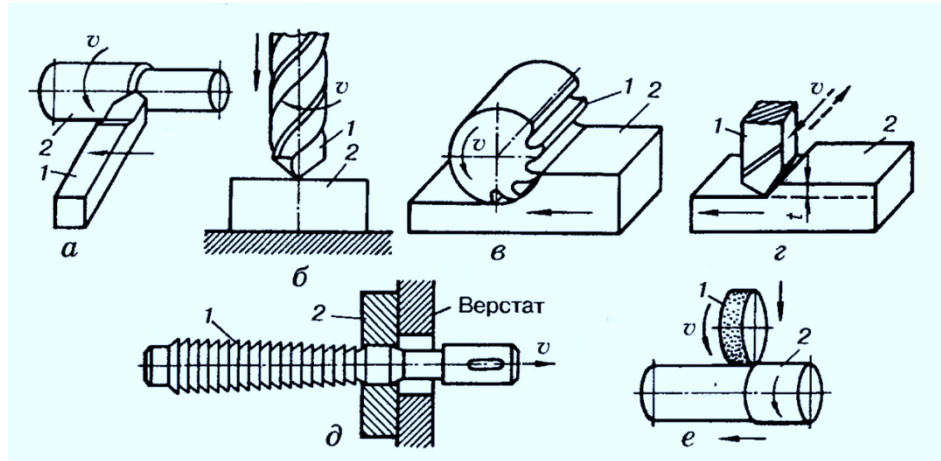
Схеми основних методів обробки різанням: а) - точіння, б) - свердління, в) - фрезерування, г) - стругання, д) - протягання, е) - шліфування
